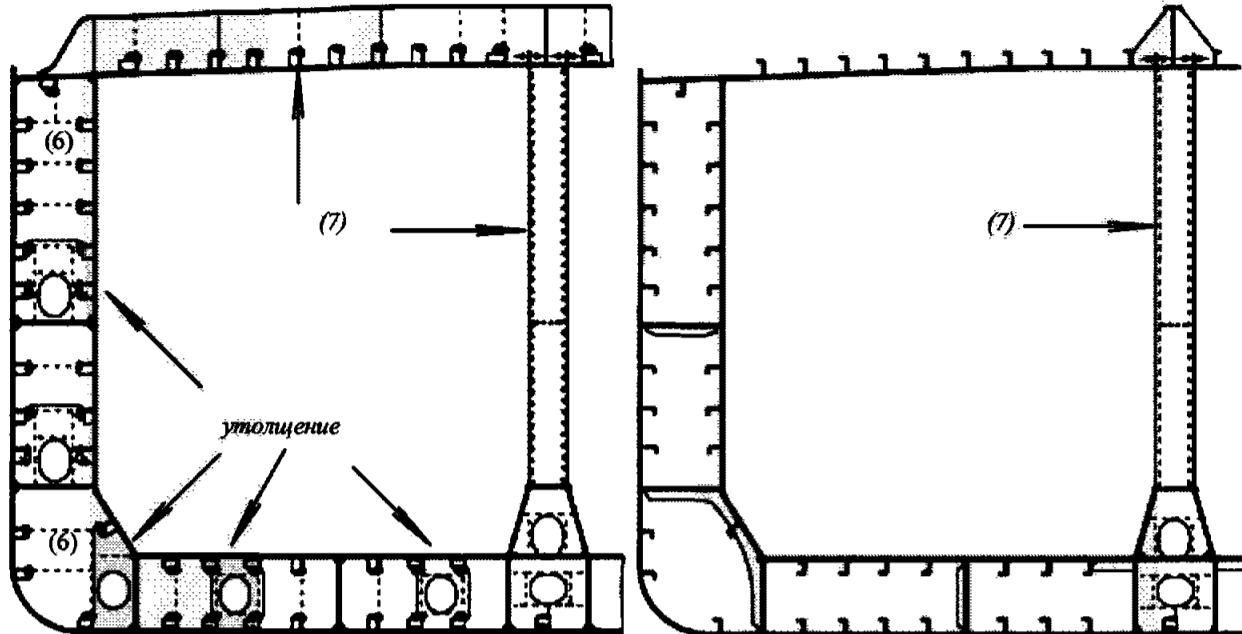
Типовое поперечное сечение химовоза (DW около 10000).
